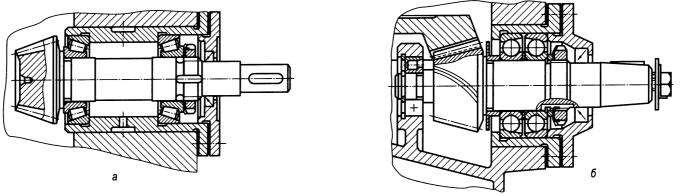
Вал-шестерня конической зубчатой передачи с консольным (а) и неконсольным (б) расположением шестерни
